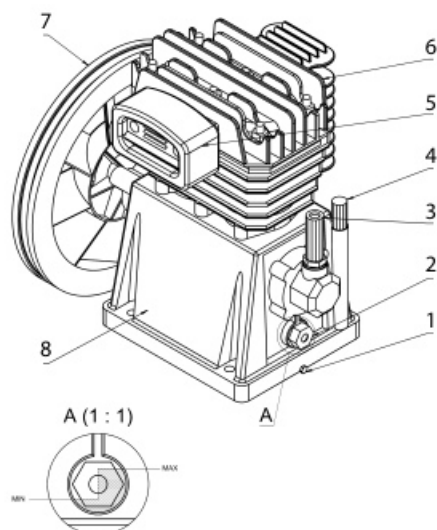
Устройство внешних узлов поршневого блока компрессоров BCB-50-440, BCB-100-440
